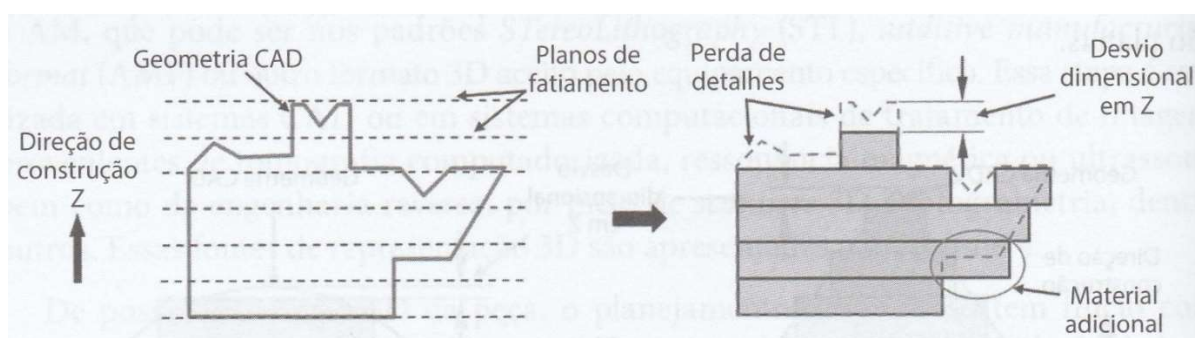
Perda ou alteração geométrica de detalhes na direção Z [6].
